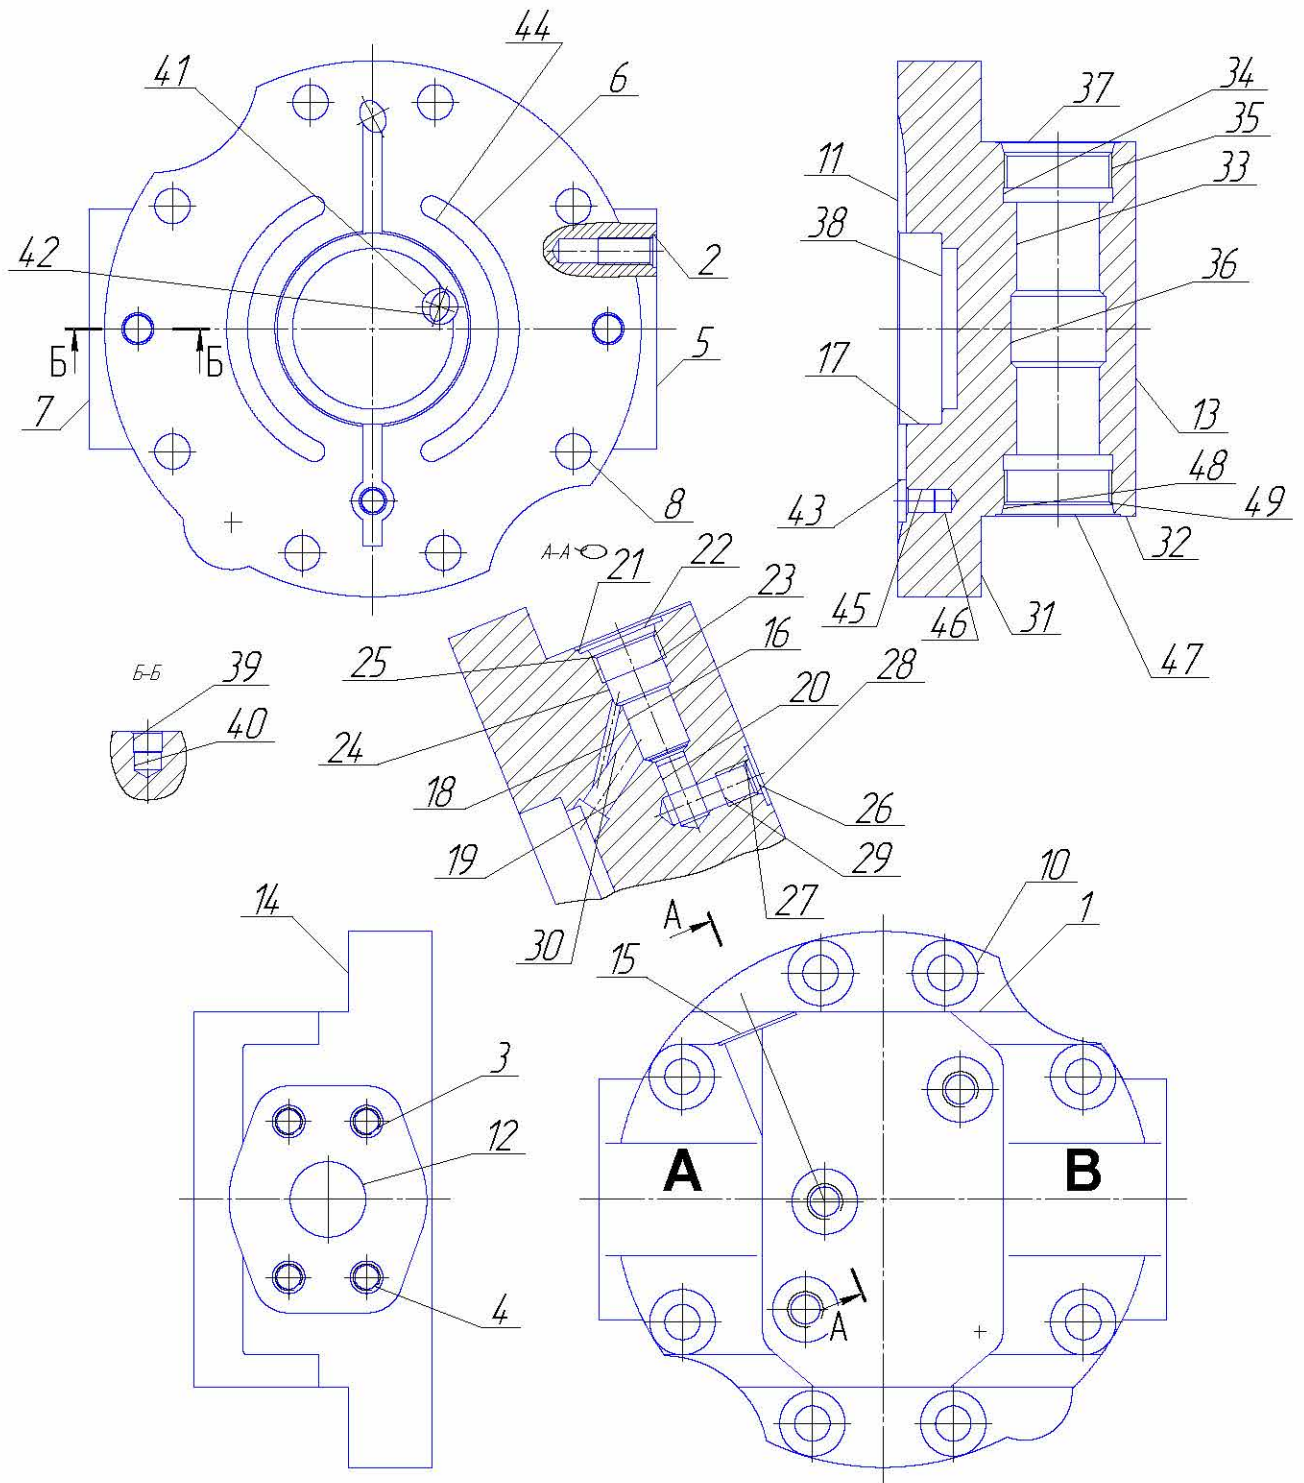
Спрощений ескіз деталі кришка задня
